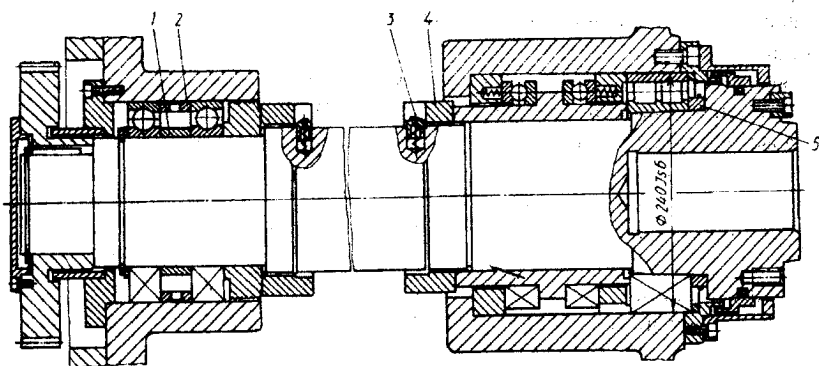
Шпиндельний вузол розточувальної бабки агрегатного верстата
